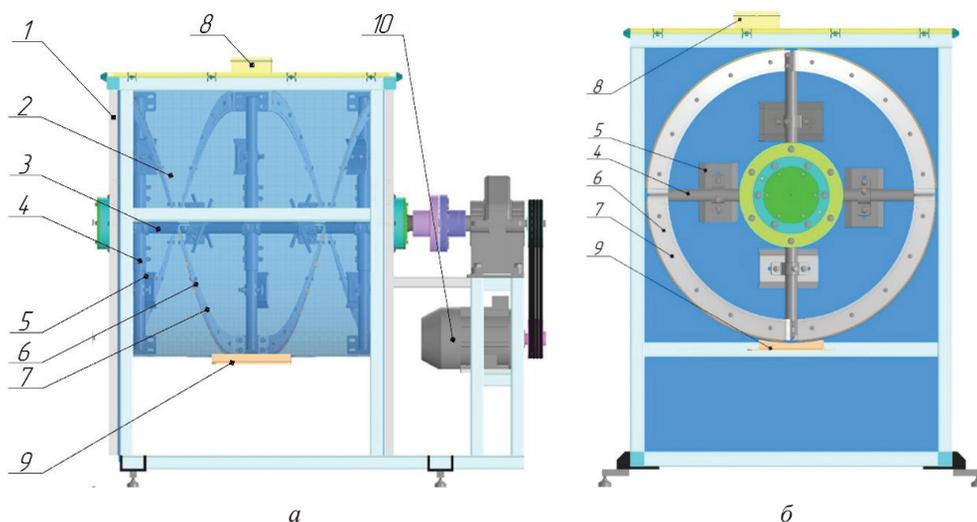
Смеситель комбикормов: *а* – общий вид; *б* – в разрезе; 1 – рама; 2 – корытообразный корпус; 3 – вал; 4 – стойка; 5 – лопатка; 6 – мешалка; 7 – резиновый элемент; 8 – загрузочное окно; 9 – выгрузная горловина; 10 – привод
